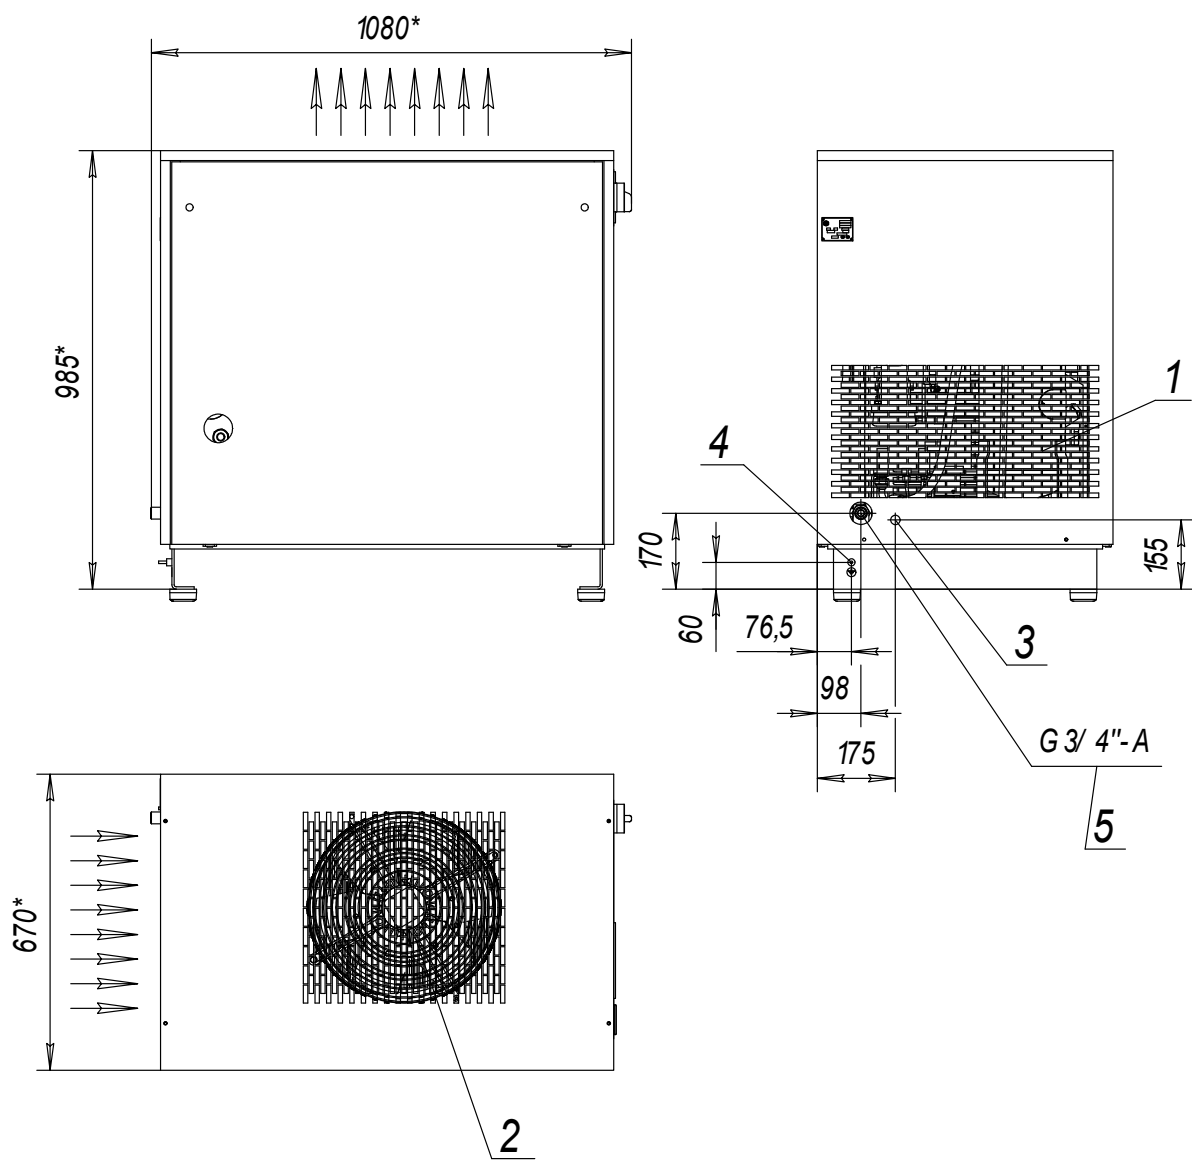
Общий вид компрессорной установки ВК20Е-8(10, 15)
